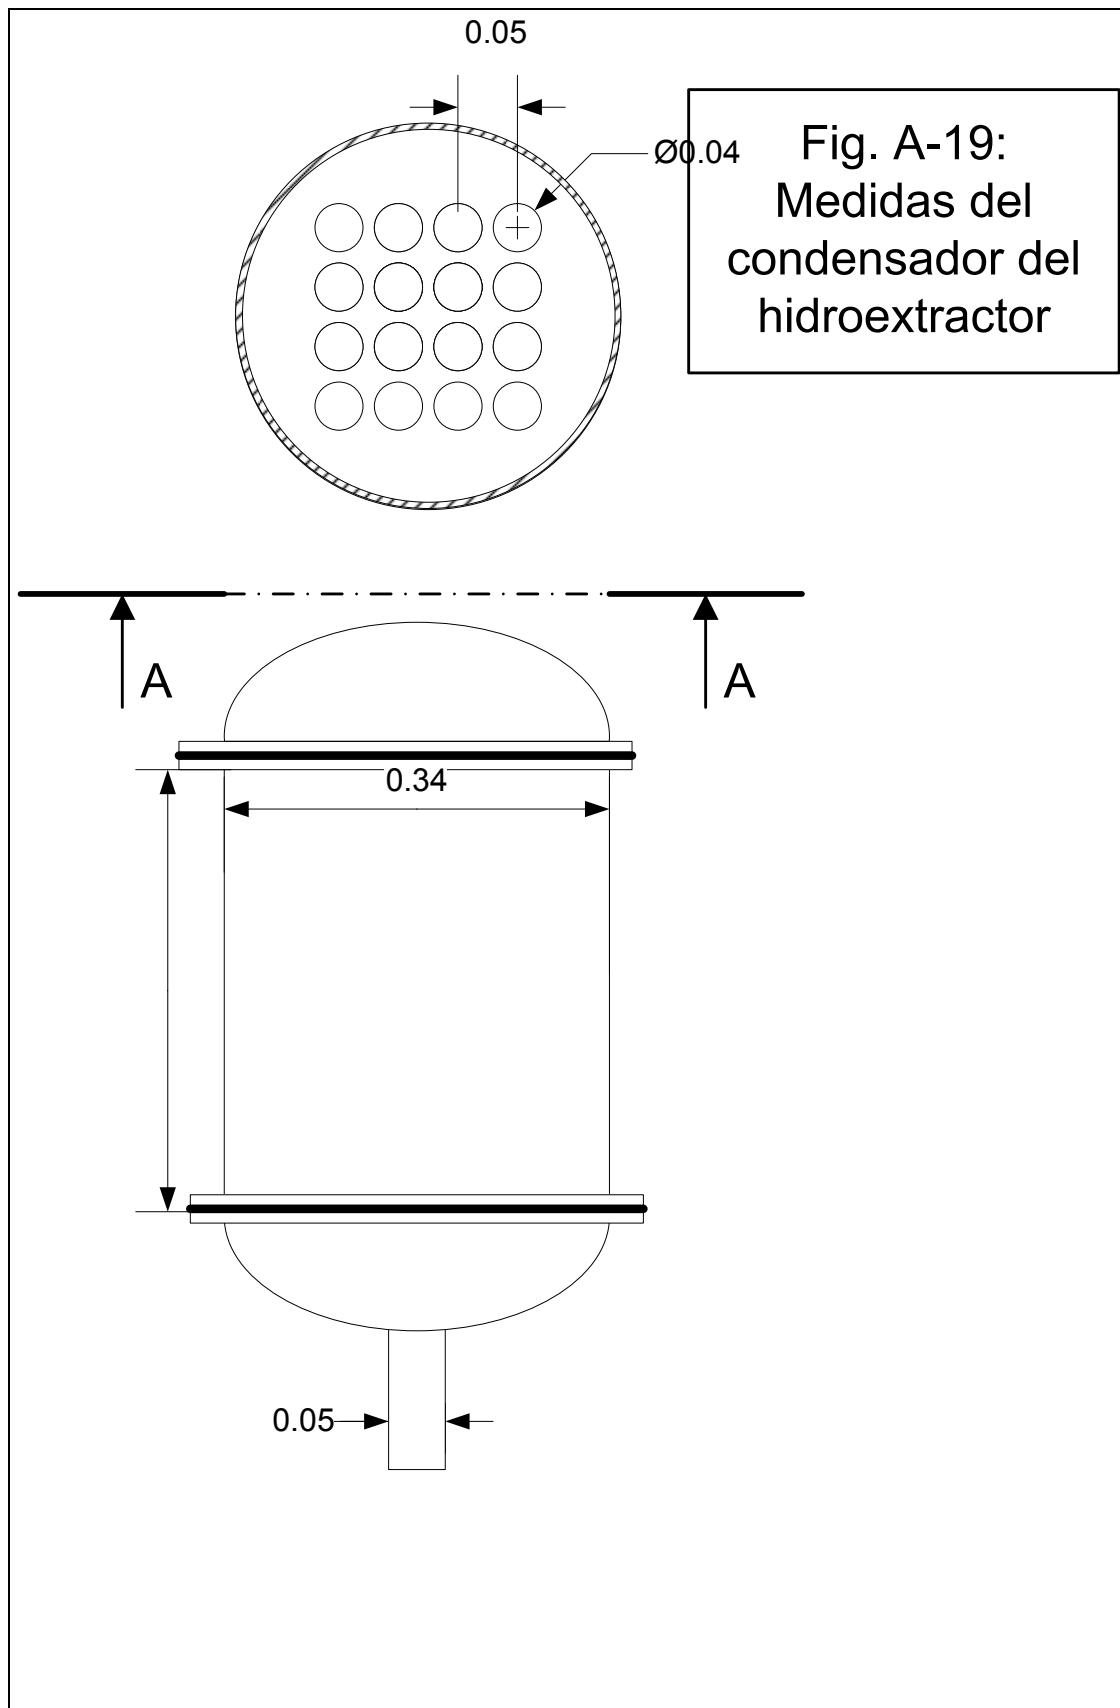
Dimensionado del Condensador del hidroextractor.
